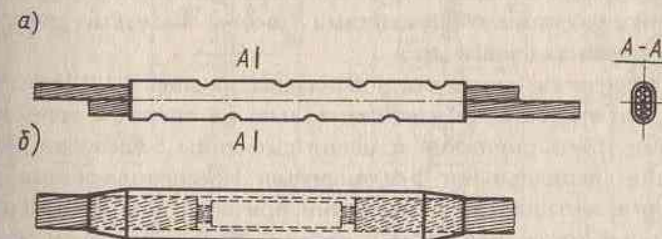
Обжимаемый овально-трубчатый и прессуемый соединители сталеалюминиевых проводов
